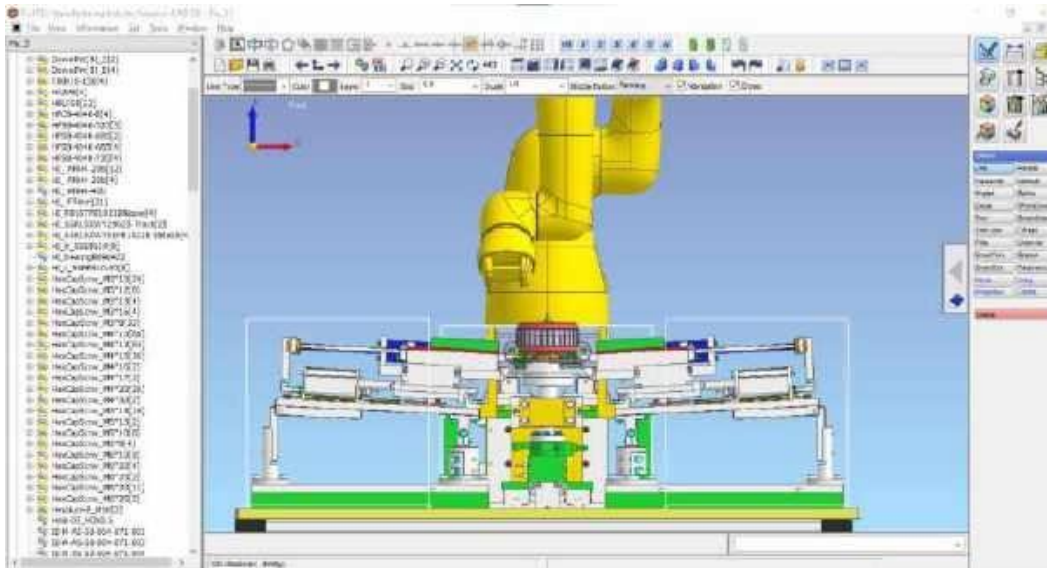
5 Spring Jig Assembly RCF N100 With Collaborative Robot
